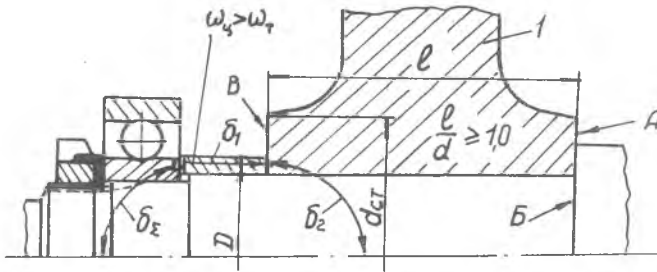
Крепление в упор к торцу вала колеса с длинной ступицей, кольца и подшипника
